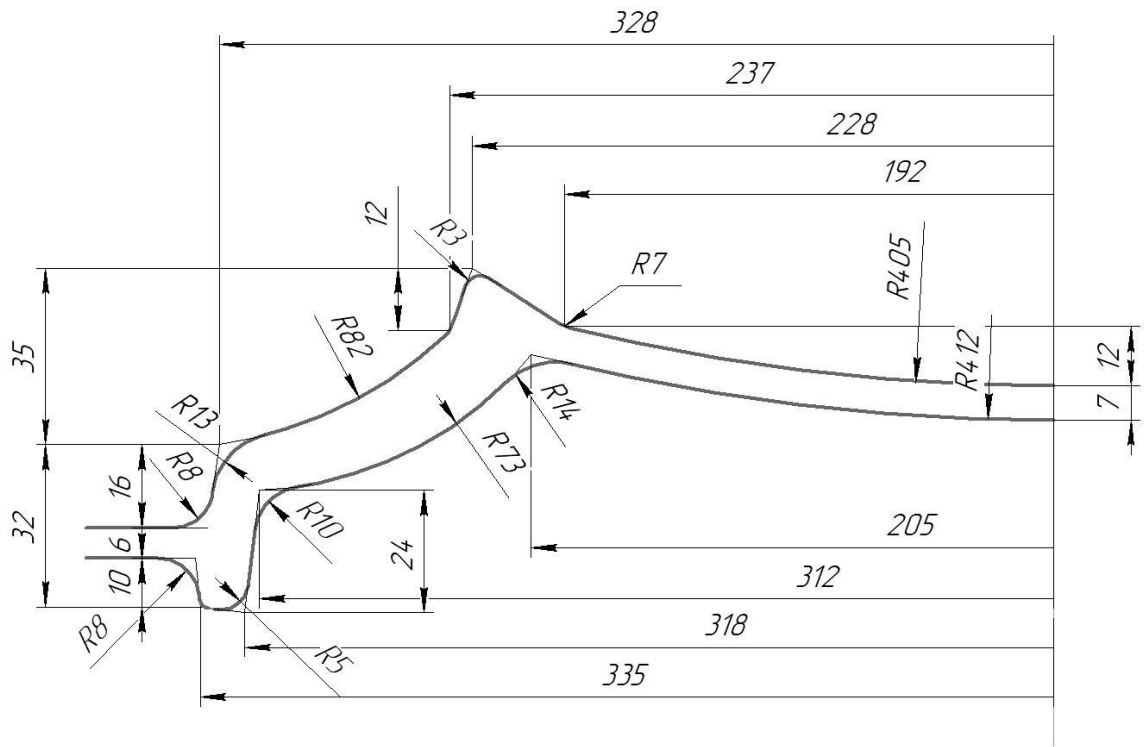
Чертеж калибра №6 (контрольный)
